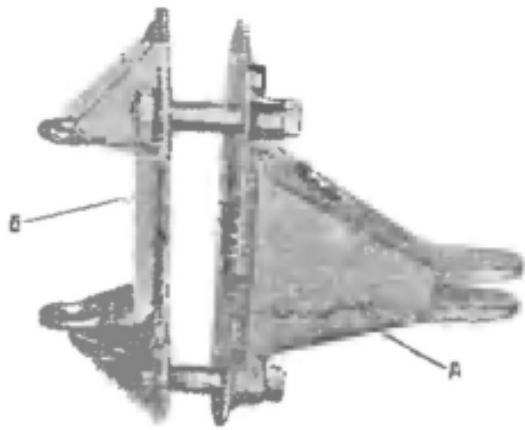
Нижний узел для подвешивания руля поворота, крепление качалок руля поворота и управления костылем.
